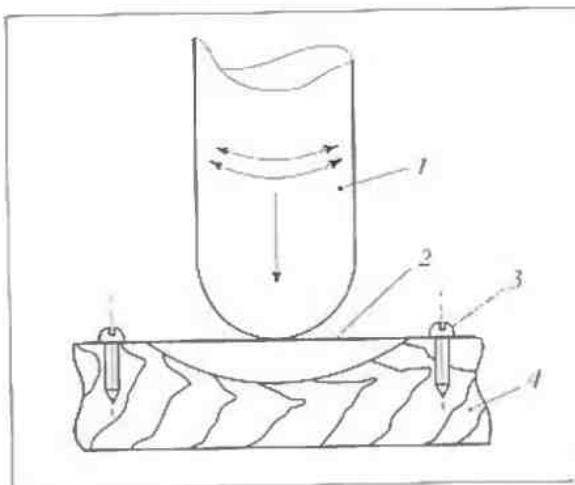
Изготовление чашечки: 1 – круглая палочка-“пансон” (руковитка стамески); 2 – фольга; 3 – шурупы; 4 – матрицы
